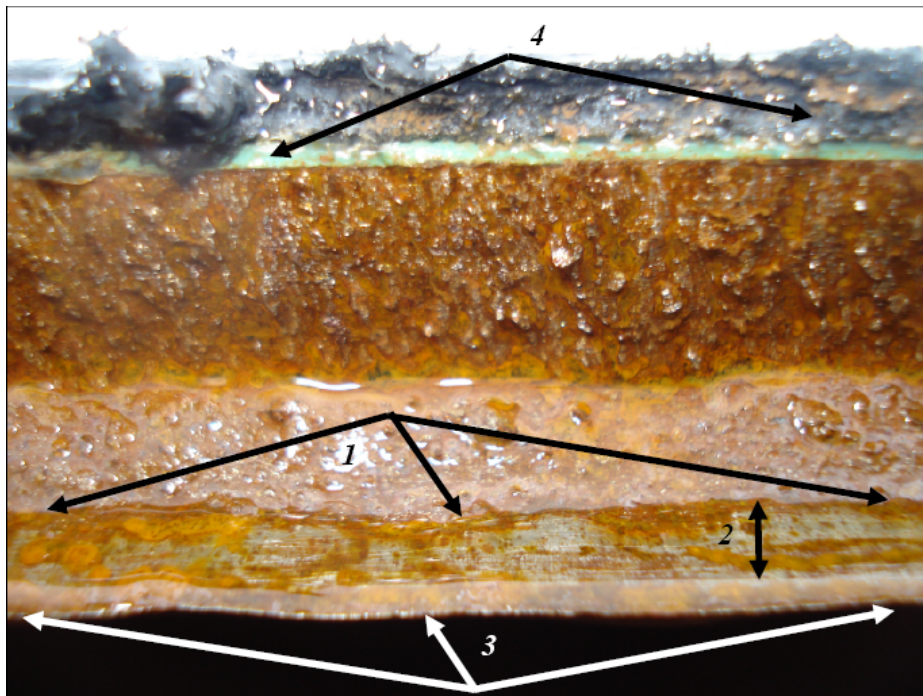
Дефекты сварного соединения в области разрыва трубы: 1 – дефект несплавления основного металла трубы и внутреннего продольного сварного шва, 2 – глубина зоны несплавления, 3 – дефект наплыва металла внутреннего сварного шва на поверхность трубы, 4 – наружная изоляция трубы
